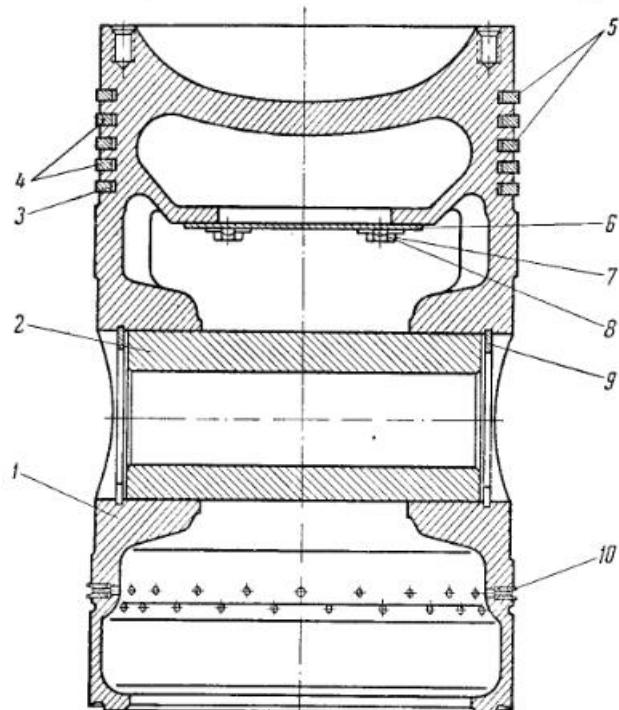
Поршень (в сборе) двигателей типа NVD-48:
